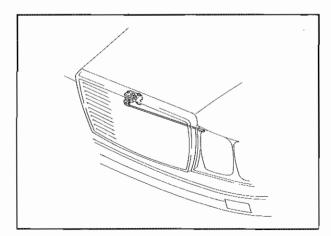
Serratura cofano vano motore Engine bonnet lock
